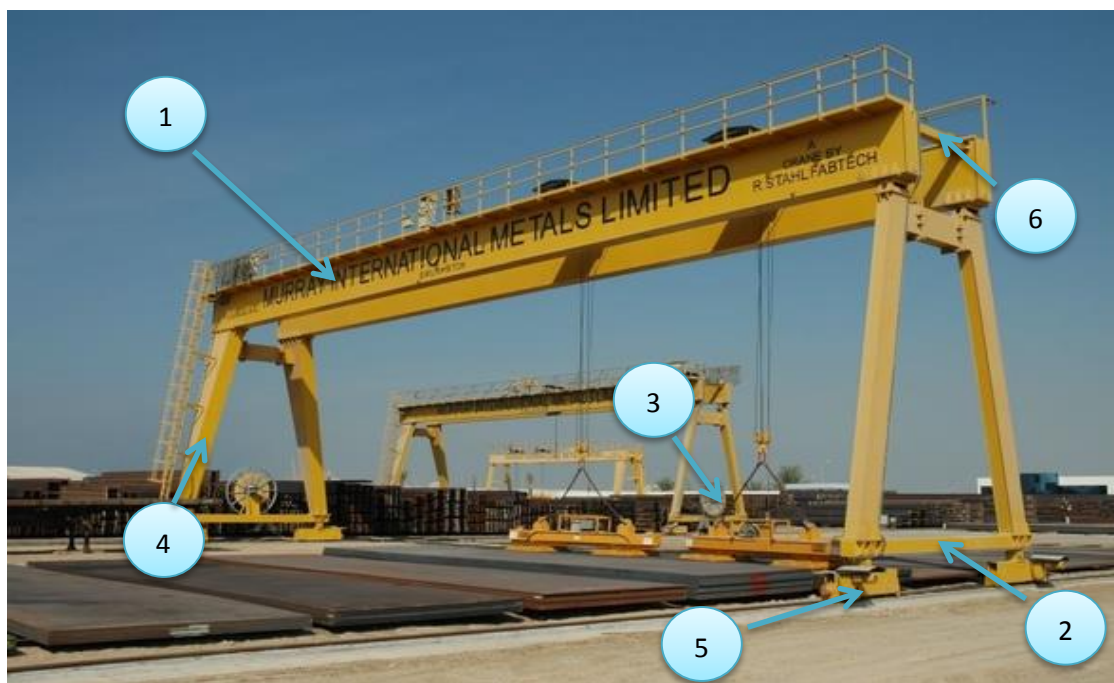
Grúa pórtico para elevar placas de acero mediante electroimanes. 1. Puente guía. 2. Testero. 3. Mecanismo de elevación. 4. Poste. 5. Paquete de rodadura. 6. Traviesa de cierre. Imagen cortesía de R. STAHL FABTECH.
